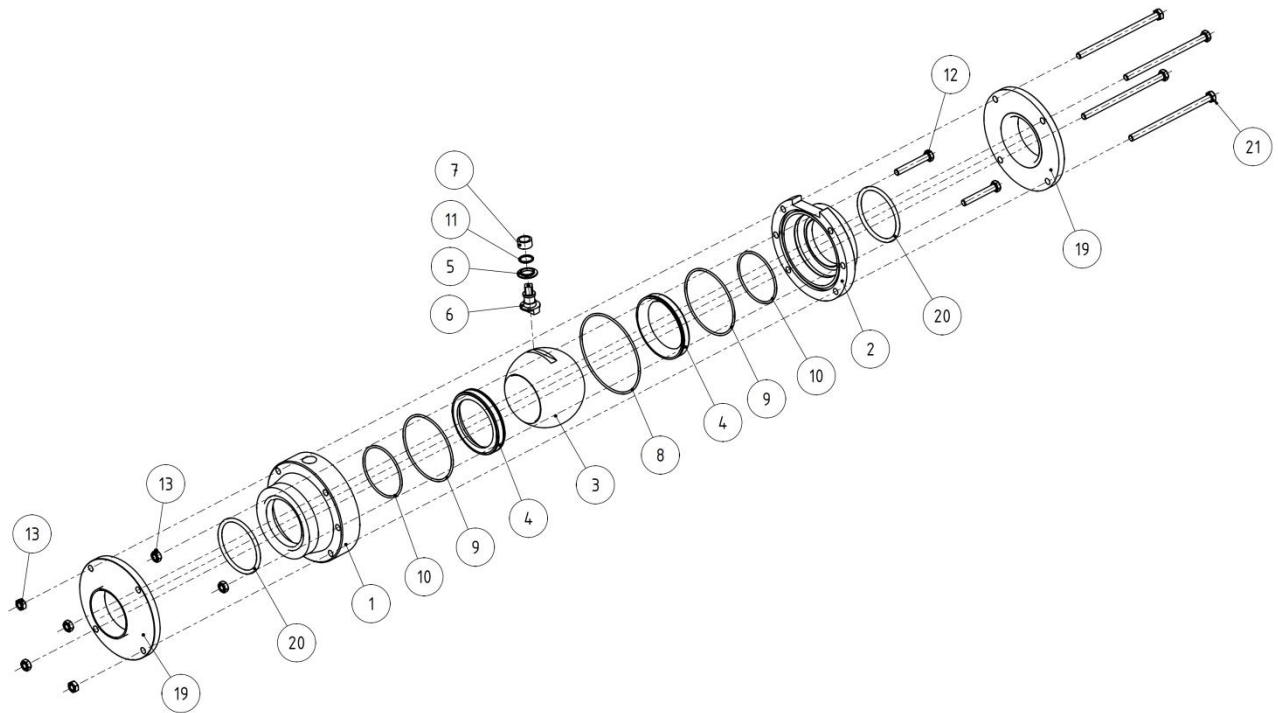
Kugelventil-ZF ohne Betätigung (Explosionsdarstellung)
